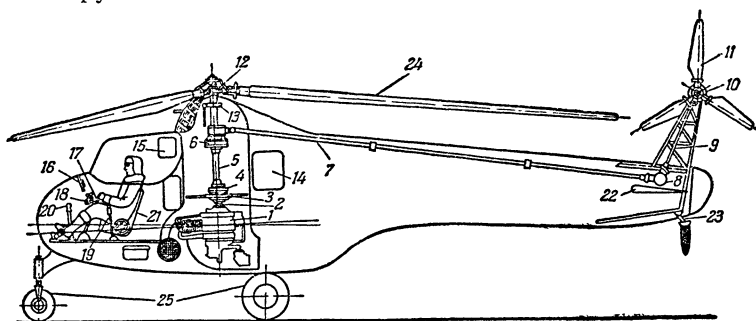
Схема устройства одновинтового двухместного вертолётa: 1 — двигатель, 2 — муфта включения, 3 — вентилятор, 4 — муфта свободного хода, 5 — карданный вал, 6 — главный редуктор, 7 — вал рулевого винта, 8 — нижний редуктор рулевого винта, 9 — верхний вал рулевого винта, 10 — верхний редуктор рулевого винта, 11 — рулевой винт, 12 — несущий винт, 13 — автомат перекоса, 14 — бензобак, 15 — радиоустановка, 16 — приборная доска, 17 — ручка управления, 18 — сектор газа, 19 — ручка управления шагом и дросселем, 20 — рычаг управления муфтой сцепления, 21 — два рядом установленных сиденья, 22 — стабилизатор, 23 — хвостовой костьль, 24 — лопасть несущего винта, 25 — колёса шасси.
